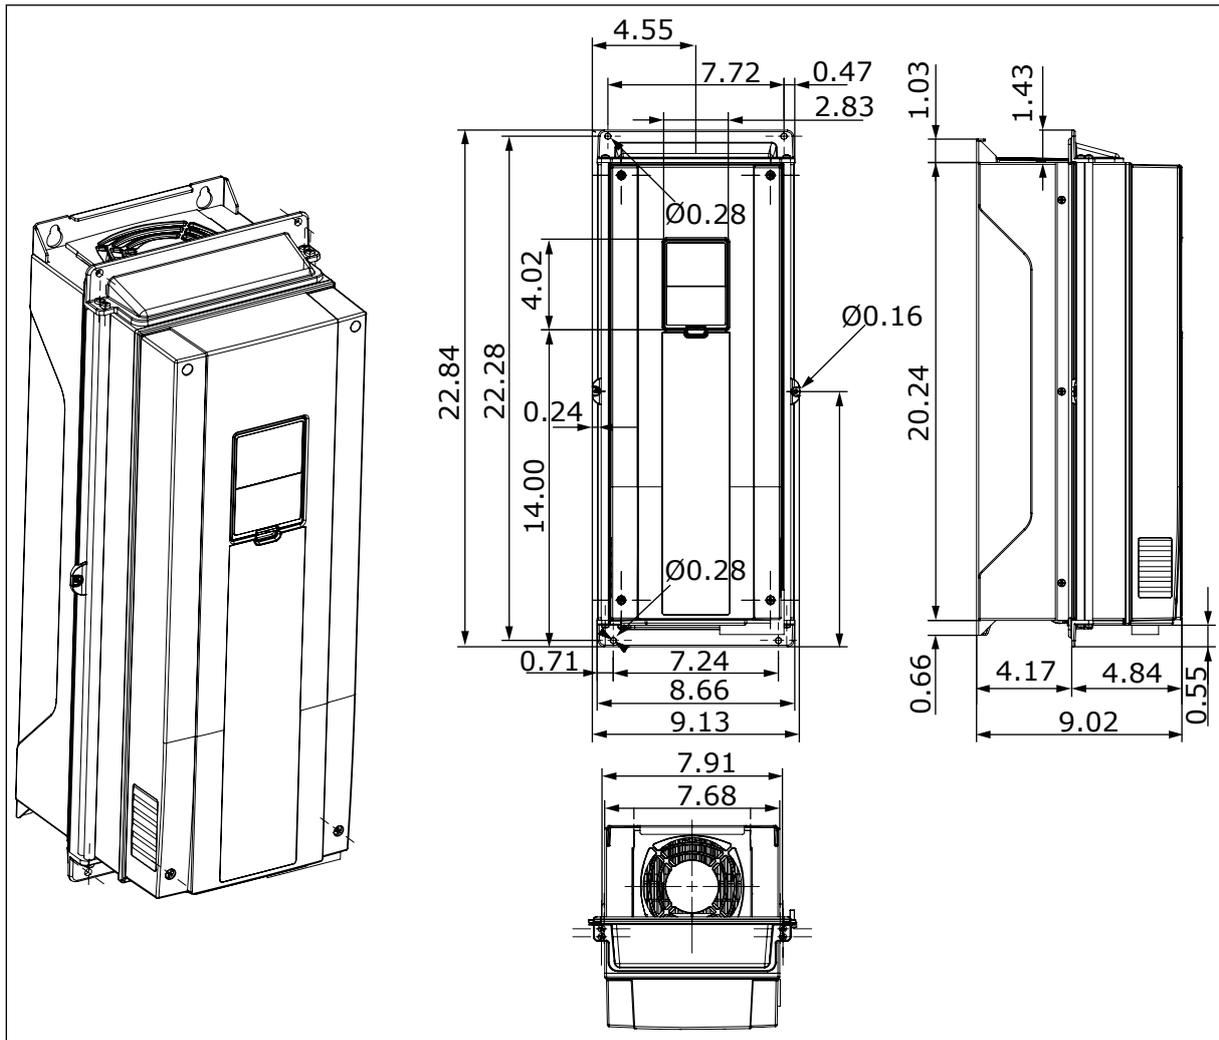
Abmessungen des Frequenzumrichters, Flanschbefestigung, MR6 [in]
